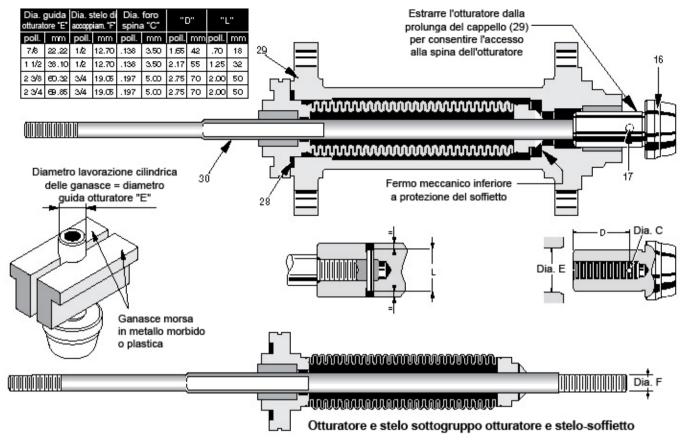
Montaggio e rimozione della spina di fissaggio dell'otturatore allo stelo
